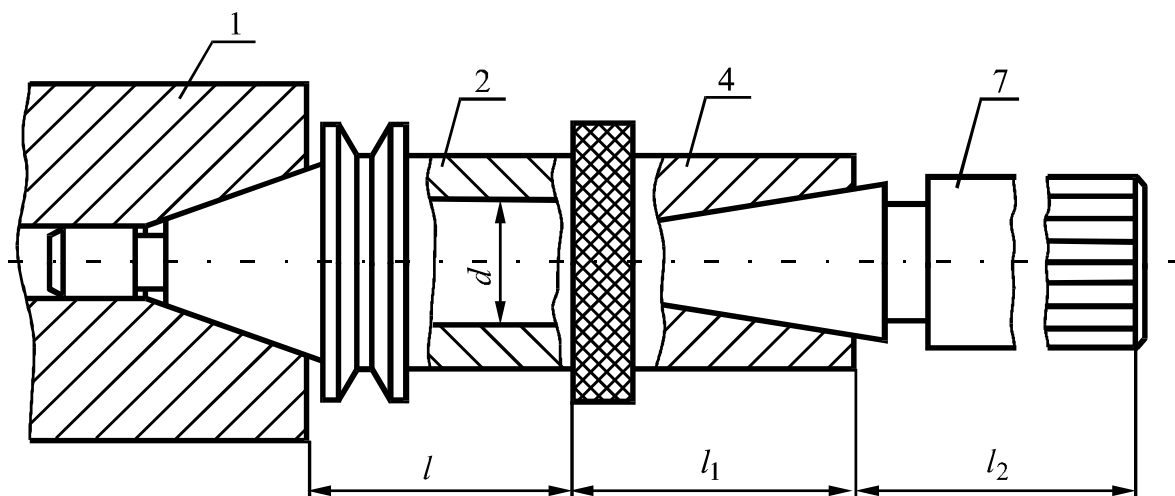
Эскиз инструментального блока для установки развертки
